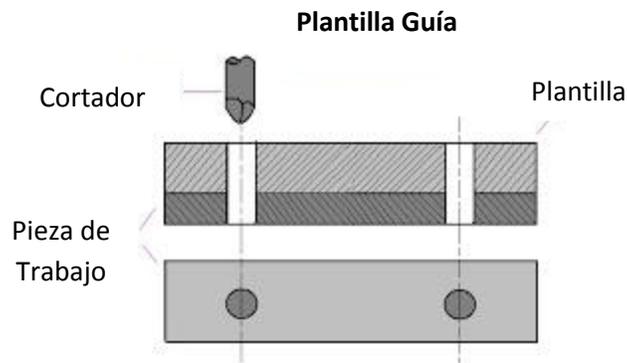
Plantilla de sujeciones. Fuente: engineeringhut.
